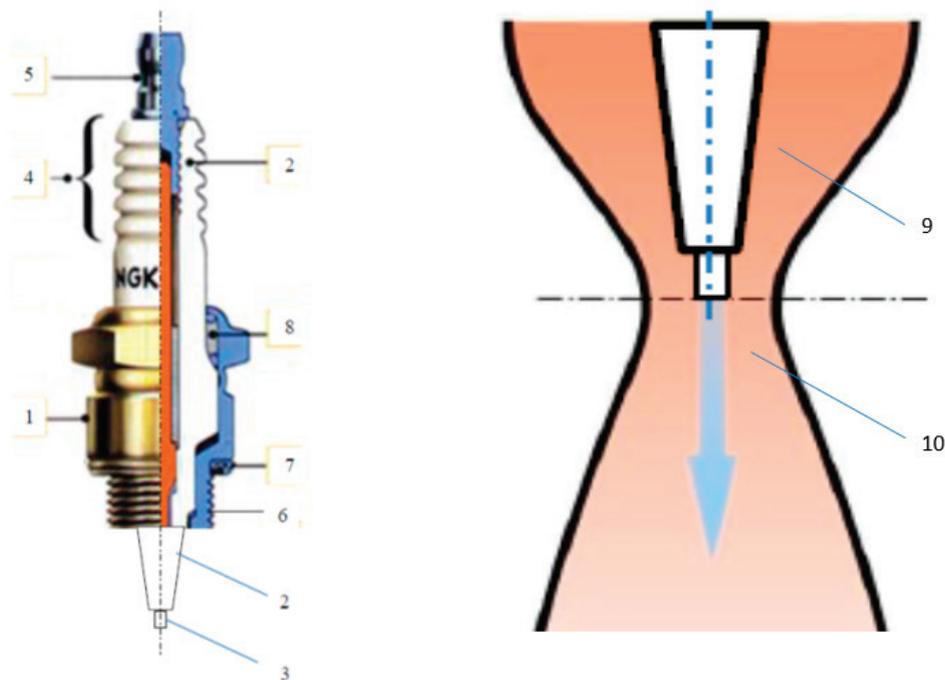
Свеча зажигания и ее подставка: 1 — металлический корпус; 2 — изолятор; 3 — центральный электрод; 4 — фиксатор; 5 — контакт для провода с высоким напряжением; 6 — резьбовая часть свечи для крепления на головку цилиндра ДВС; 7 — шайба; 8 — уплотнитель; 9 — верхняя полость; 10 — нижняя полость
